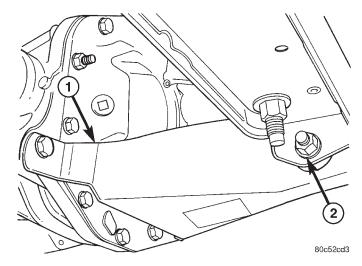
SOPORTE DEL EJE DELANTERO IZQUIERDO
